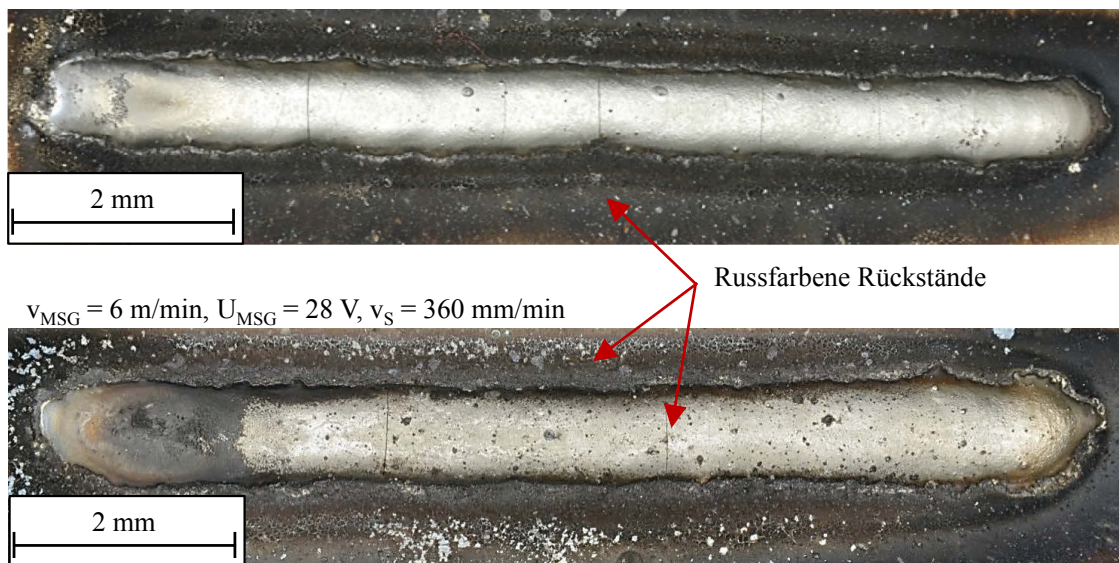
Rußfarbene Beläge auf und neben der Auftragschweißung deuten auf Verluste durch Overspray beim *MSG*-Auftragschweißen hin.
